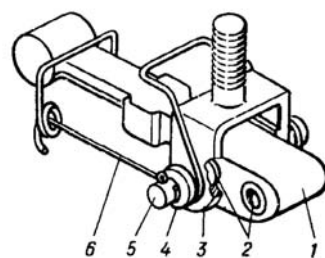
Разборка отжимного рычага: 1 — рычаг; 2 — втулка; 3 — вилка; 4 — шайба; 5 — палец; 6 — пружина
